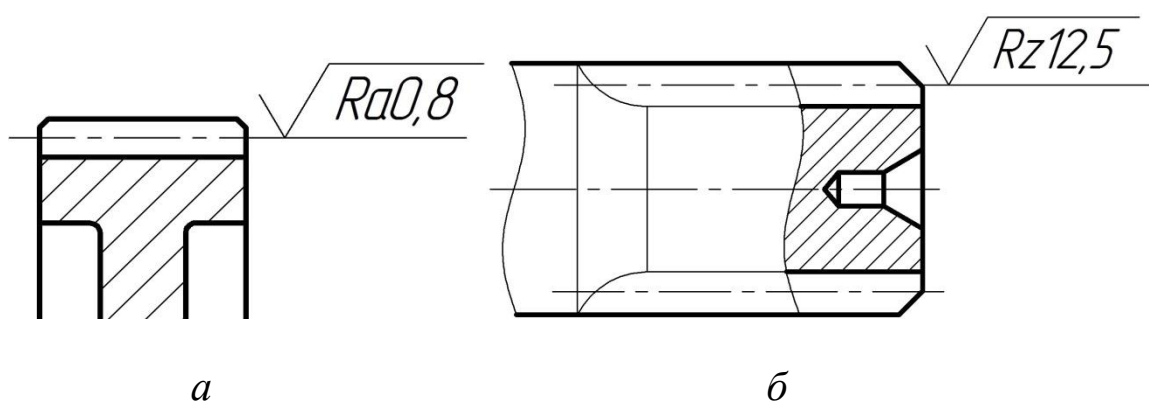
Обозначение шероховатости рабочей поверхности зубьев зубчатых колес (*а*) и эвольвентных шлицев (*б*)
